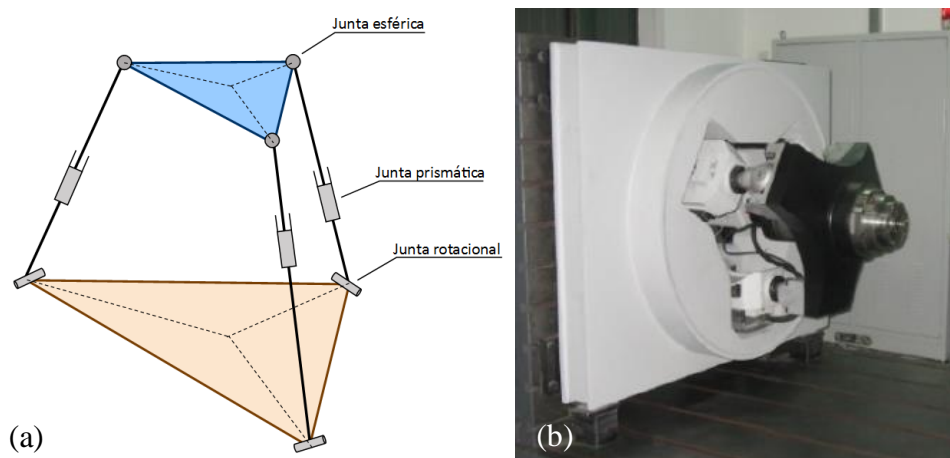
(a) Esquema de um mecanismo 3-RPS, (b) Robô A3 Tool Heads.
